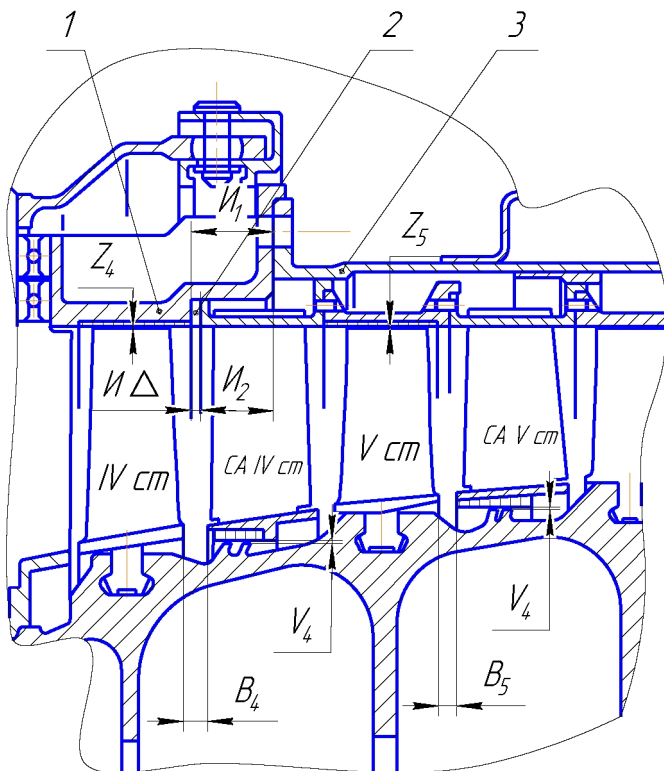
Схема расположения радиальных и осевых зазоров в проточной части компрессора
